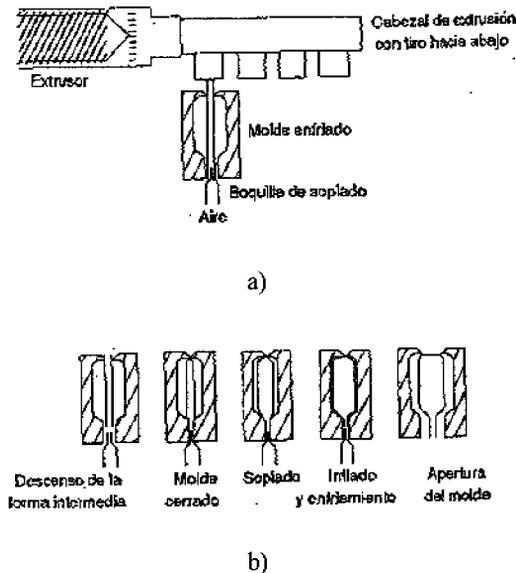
a) Forma común de moldeo por extrusión soplado.
